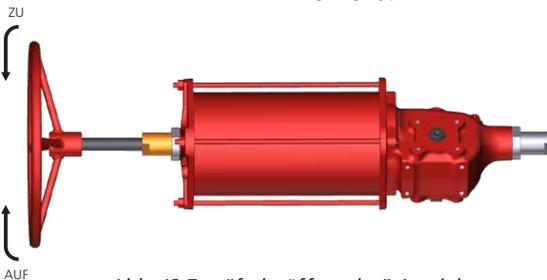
"federöffnender" Antrieb mit Handnotbetätigung Type M
